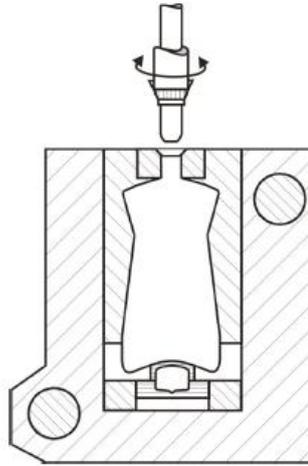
Molde de soplado y producción del cuello de las botellas mediante compresión del material por el perno de soplado.
